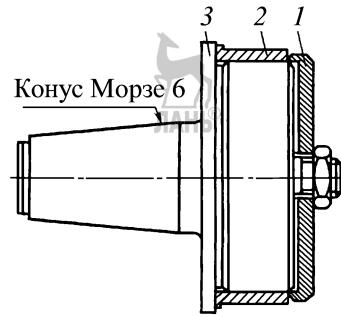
Специальная оправка для обработки заготовок типа стаканов:
